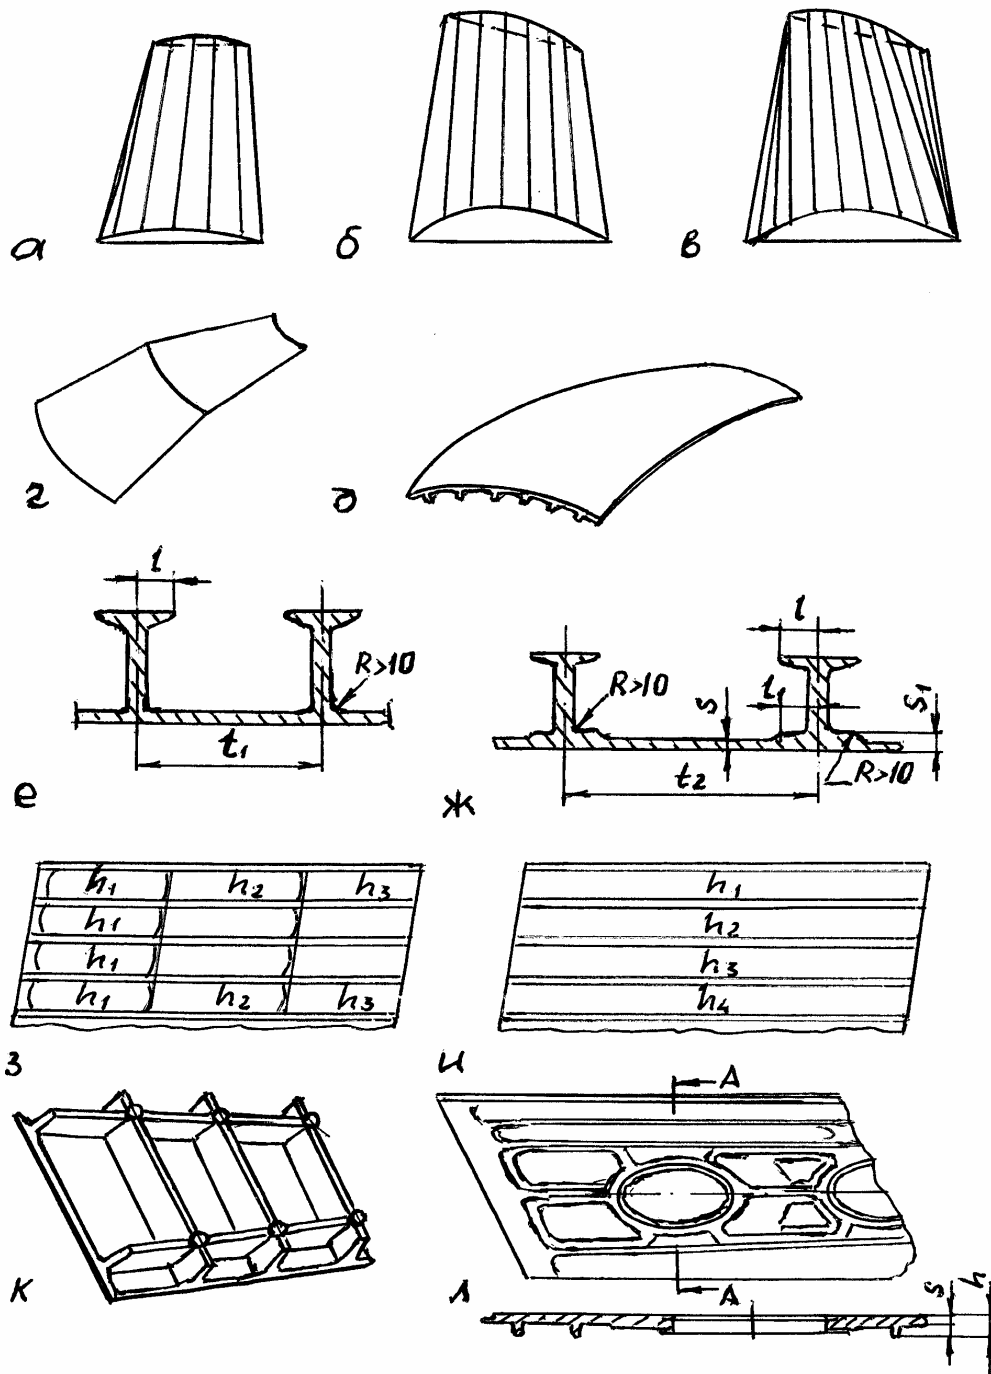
Конструктивные формы и типы монолитных панелей: а, в – линейчатые поверхности развертывающиеся без закрутки и с закруткой сечений; б - линейчатые поверхности, неразвертывающиеся с закруткой сечений; г – с линейчатой образующей с перегибом по размаху; д – с криволинейной образующей; е, ж – сопряжение ребер жесткости с полотном панели; з – со ступенчато-переменной толщиной полотна, изменяющейся в направлении ребер; и – с изменением толщины полотна в направлении, перпендикулярном ребрам; к – «вафельная», полученная прокаткой; л – фрагмент панели крыла самолета Ан-124-100
